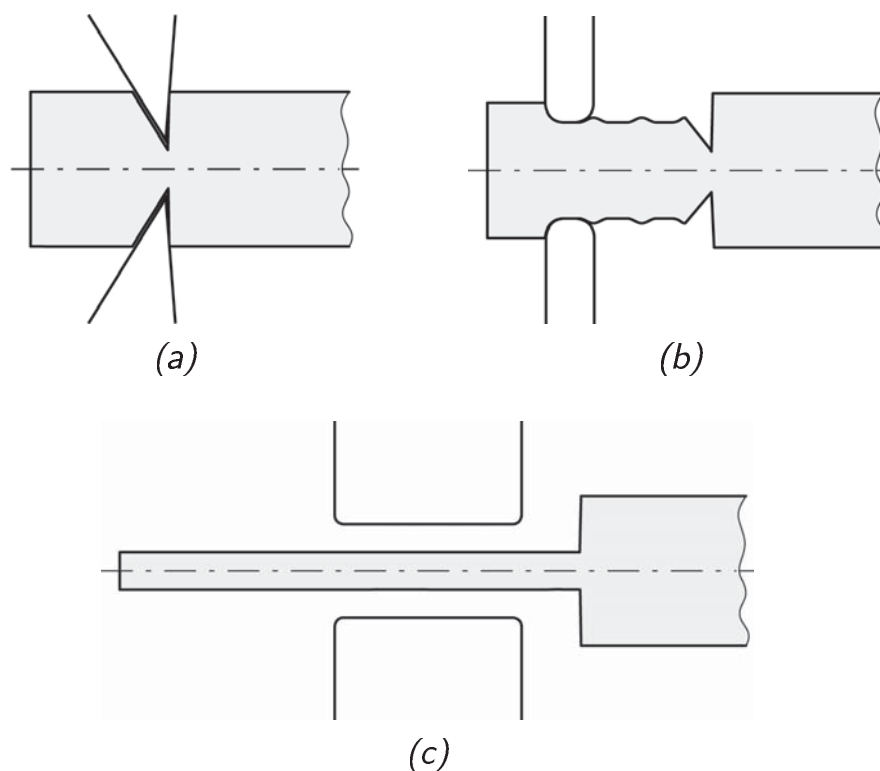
Bild (a) zeigt eine Variante des Beißschneidens mit einseitig senkrechten Schneidkeilen. Wenn das Werkstück teilweise eingeschnitten wird, kann durch Reckumformen mit einem Ballsattel, das Halbzeug gelängt (Bild (b)) und anschließend mit einem Flachsattel geschlichtet (Bild (c)) werden. Hierdurch wird ein scharfer Absatz beispielsweise für eine Welle geschaffen.
